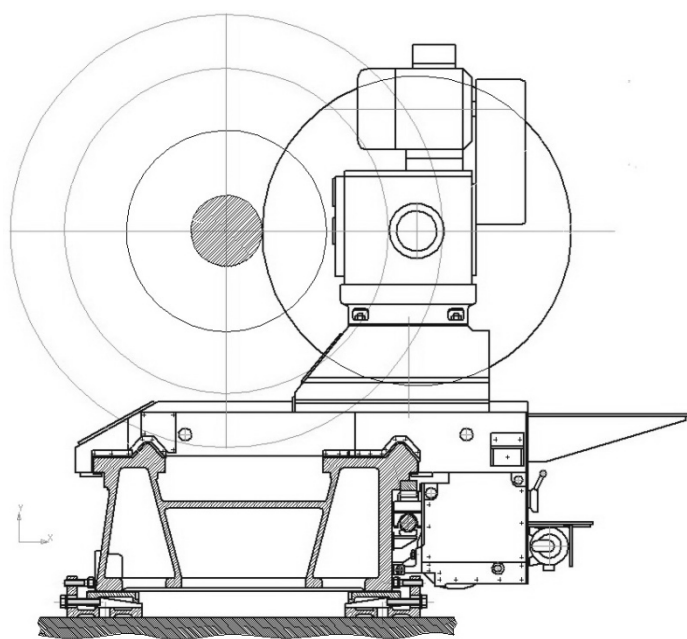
Схема модернизации станка модели КЖ16119Ф2 под фрезерование глубоких пазов ротора турбины (вид сбоку).
